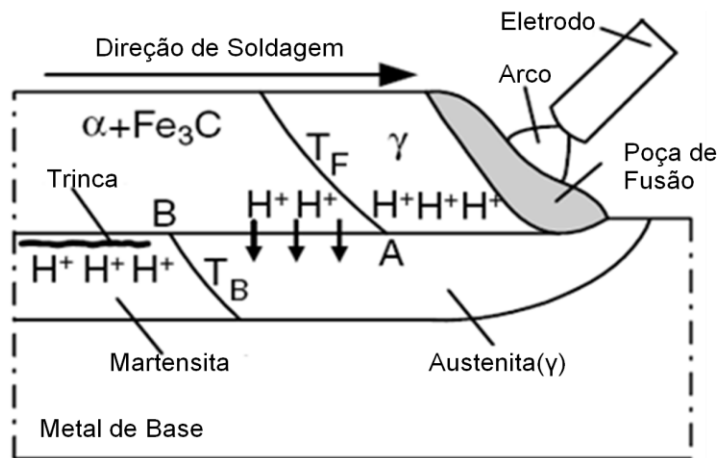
9: Difusão do hidrogênio do metal de solda para a ZTA durante a soldagem.
